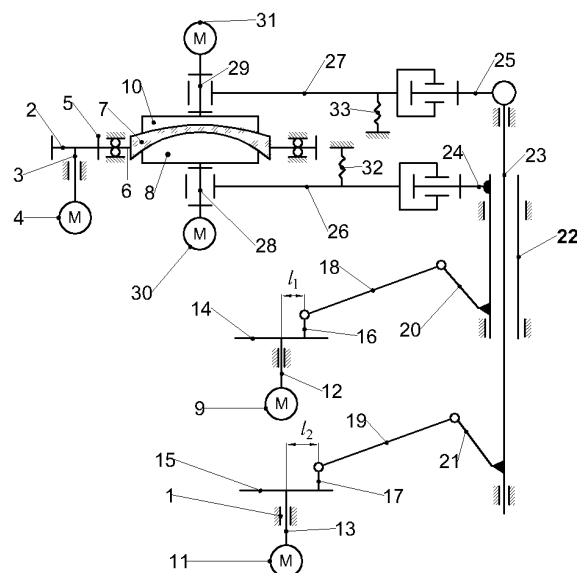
Кинематическая схема станка для двусторонней обработки линз
